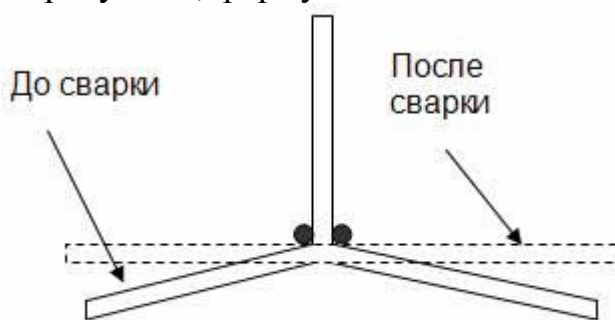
11. Обратный изгиб деталей перед сваркой.
